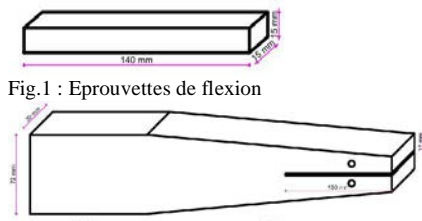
Eprouvettes pour l'essai de fissuration
